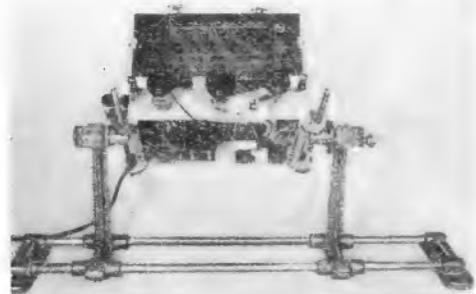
Universal-Reparatur-Rahmen mit Chassis
